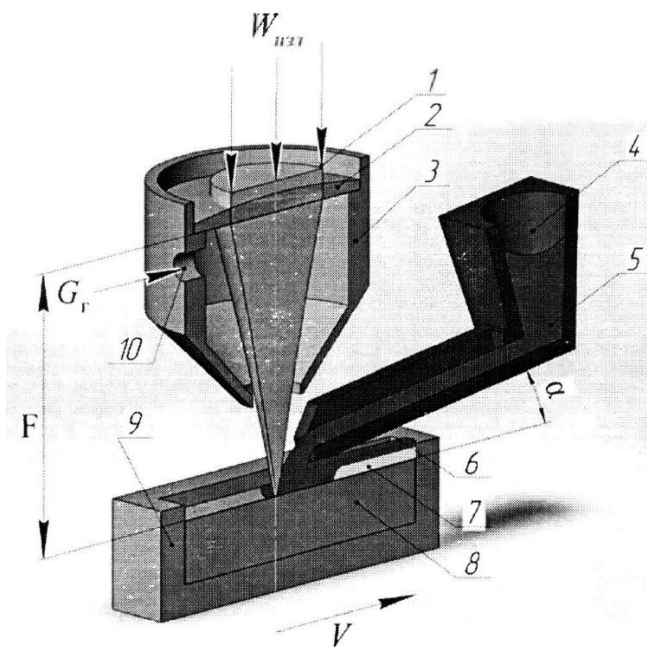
Технологічна схема лазерно-ливарного методу виготовлення біметалів: 1 - лазерне випромінювання; 2 - лінза; 3 - сопло; 4 - лоток; 5 - розплав; 6 - поверхневий шар; 7 - твердий шар; 8 - заготовка; 9 - обмежувачі; 10 - захисний газ.
